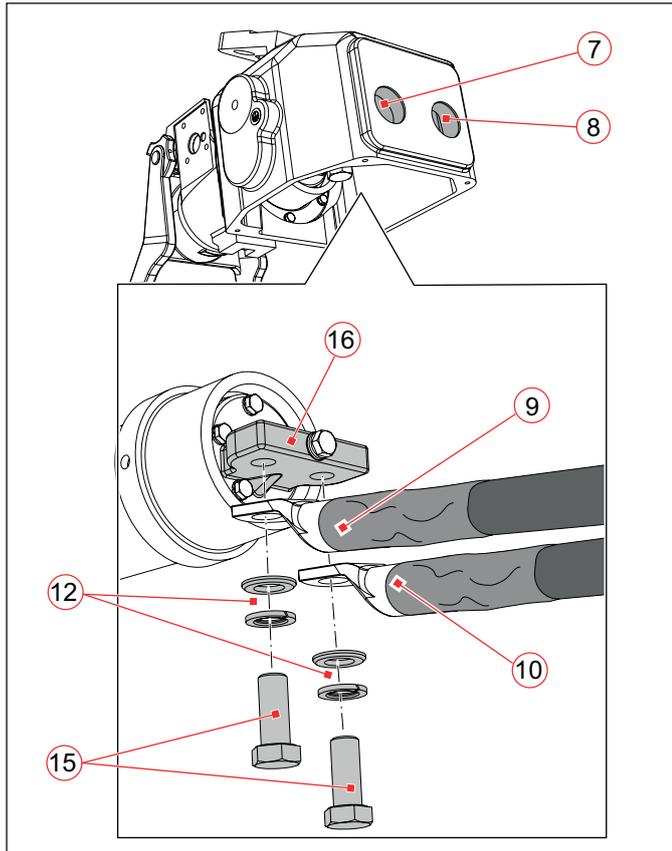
Kabelanschlüsse 2 x hinten, horizontal
